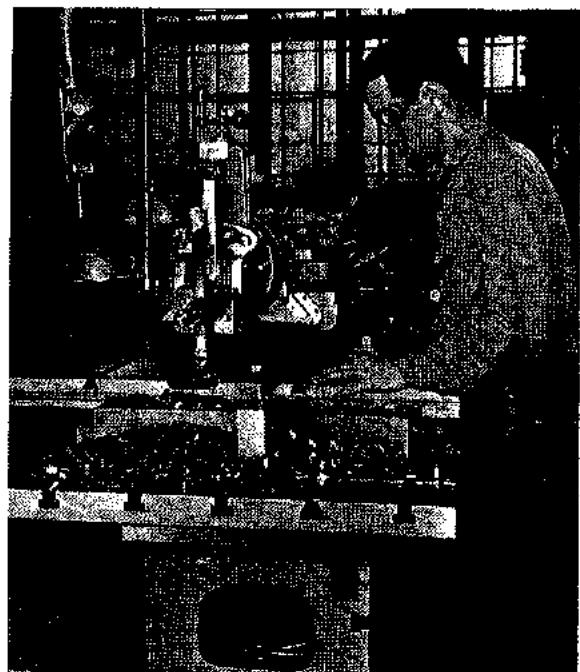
Mecanizado de una pieza sujetada directamente a la mesa de la lladadora, la cual va equipada con una sobremesa auxiliar (Cincinnati Shaper Co.)
